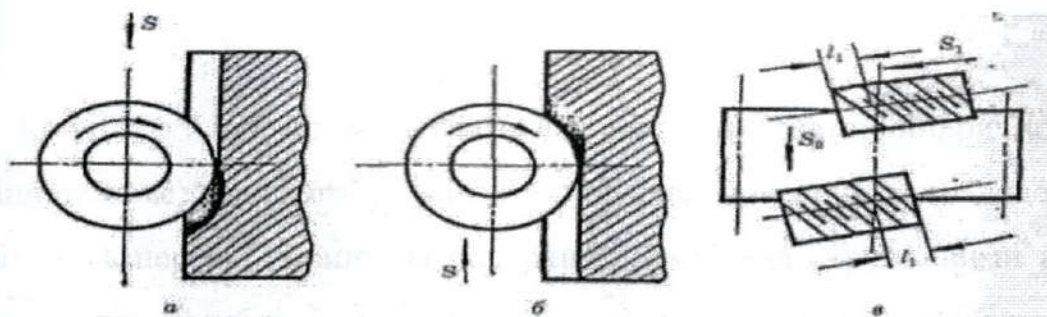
Схема зубофрезерування: а – зустрічне; б – попутне; в - діагональне
